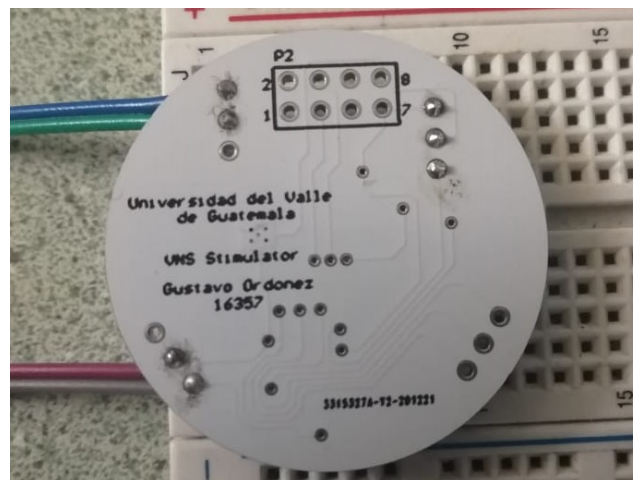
Aspecto físico del PCB fabricado, cara trasera.
